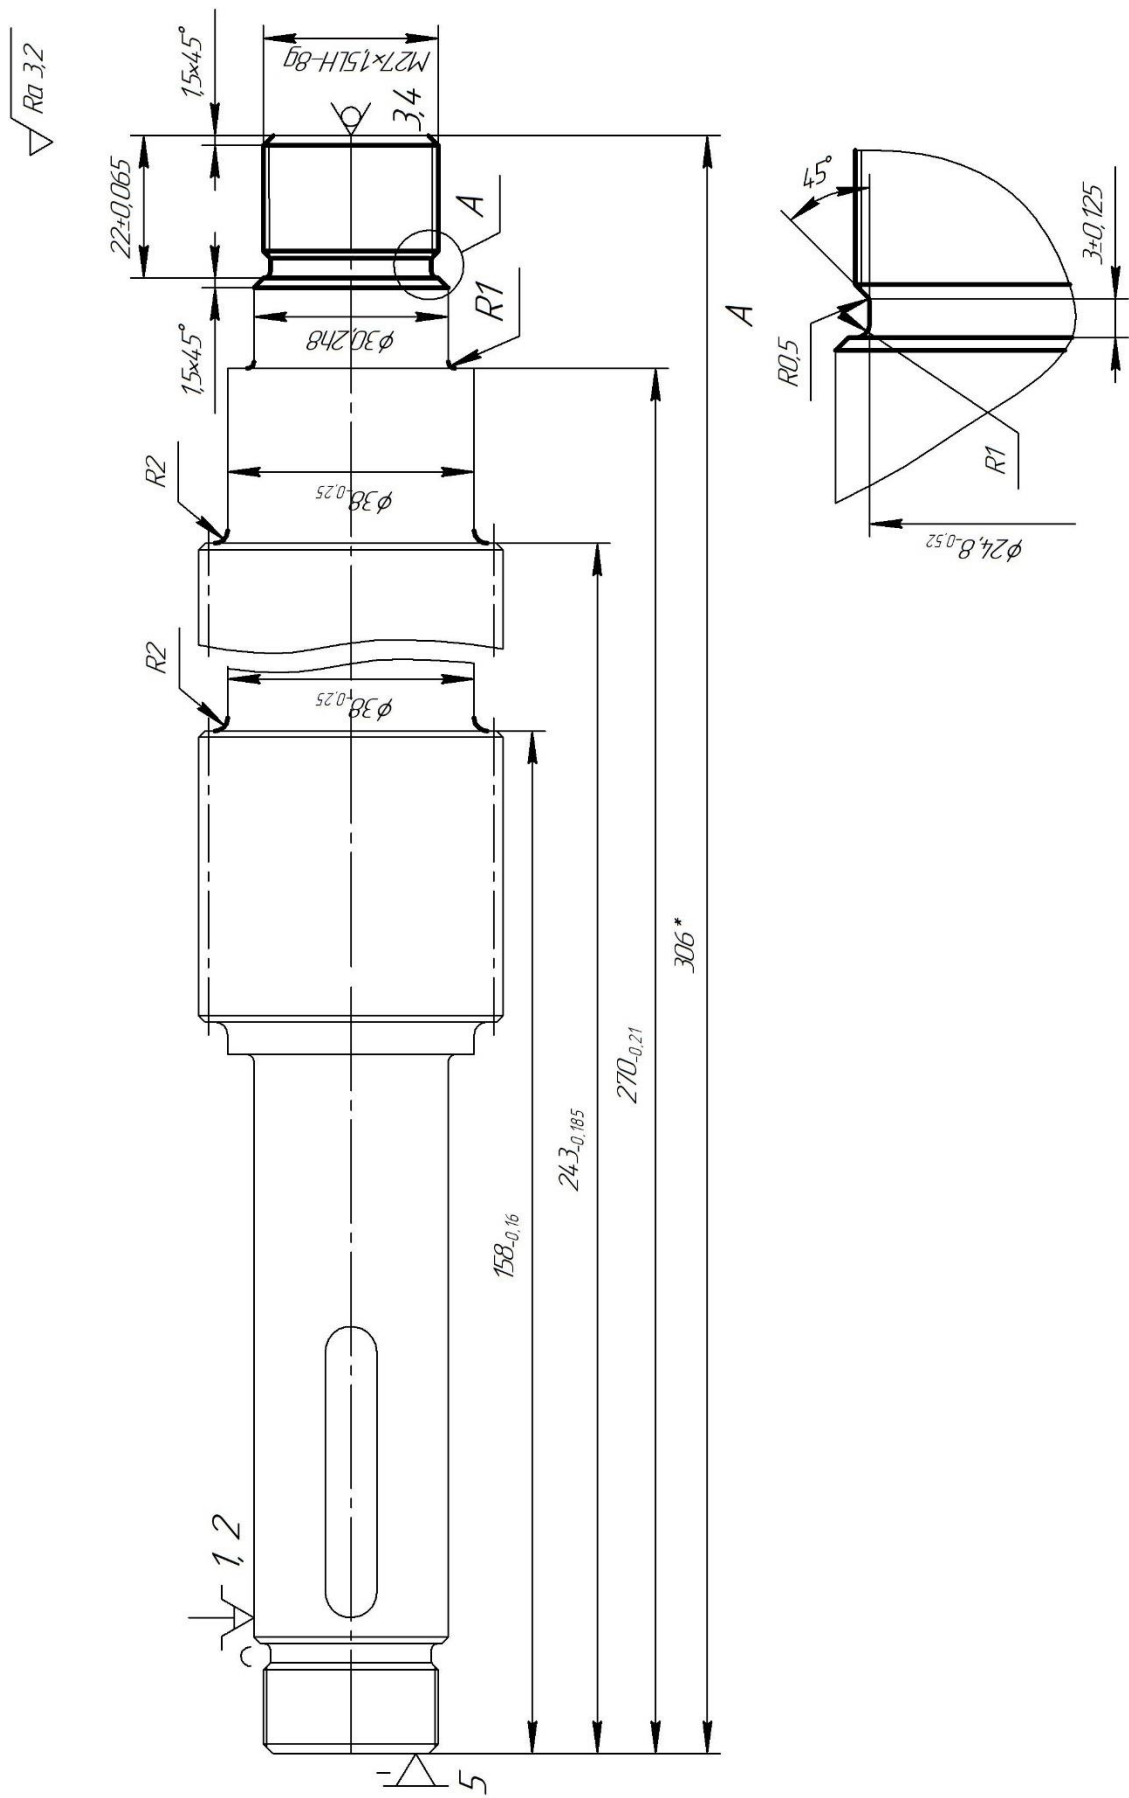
Альтернативна схема базування заготовки на операції 065 токарній з ЧПК, установ Б
